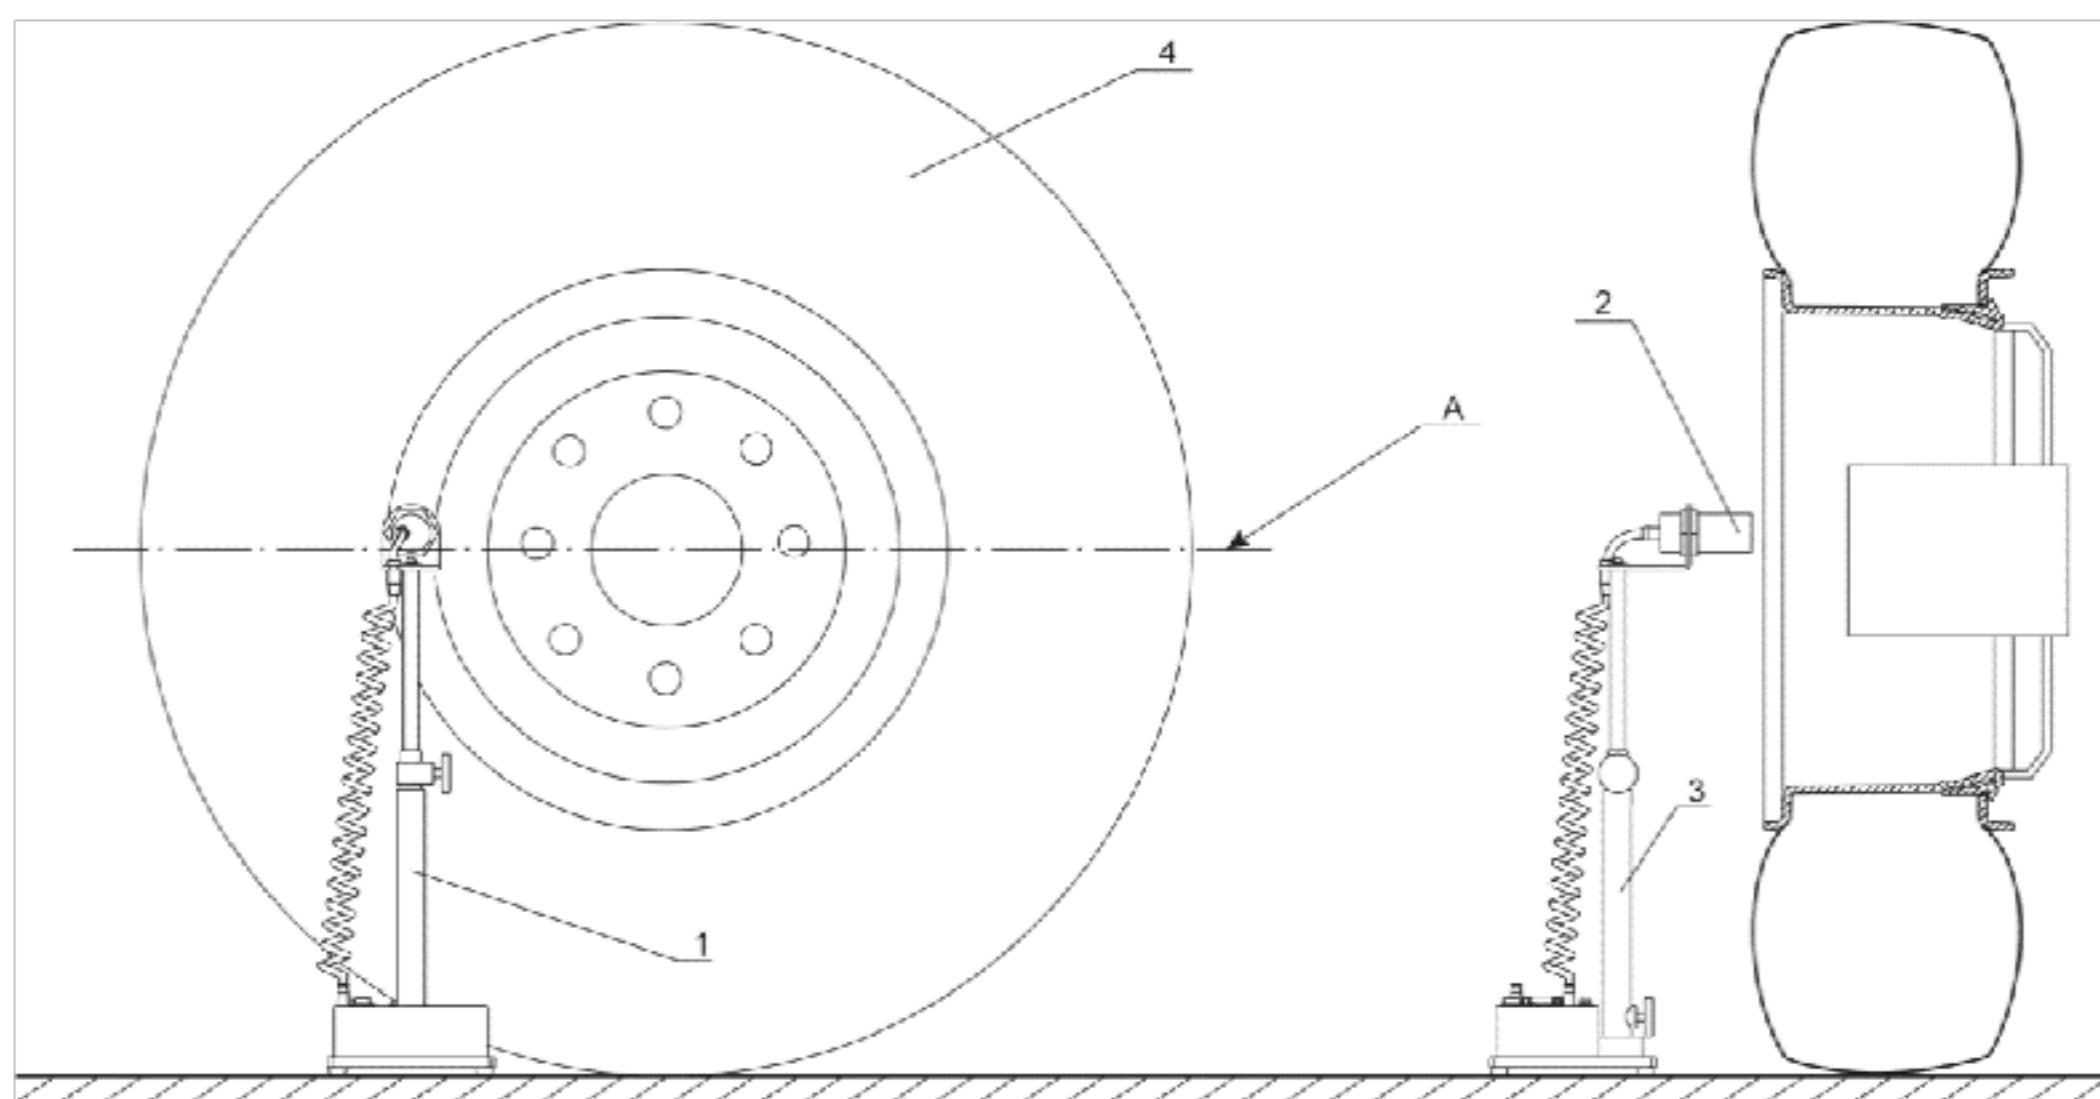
Установка датчика движения колеса: 1 - датчик движения; 2 - индуктивный преобразователь перемещения; 3 - стойка; 4 - управляемое колесо.
